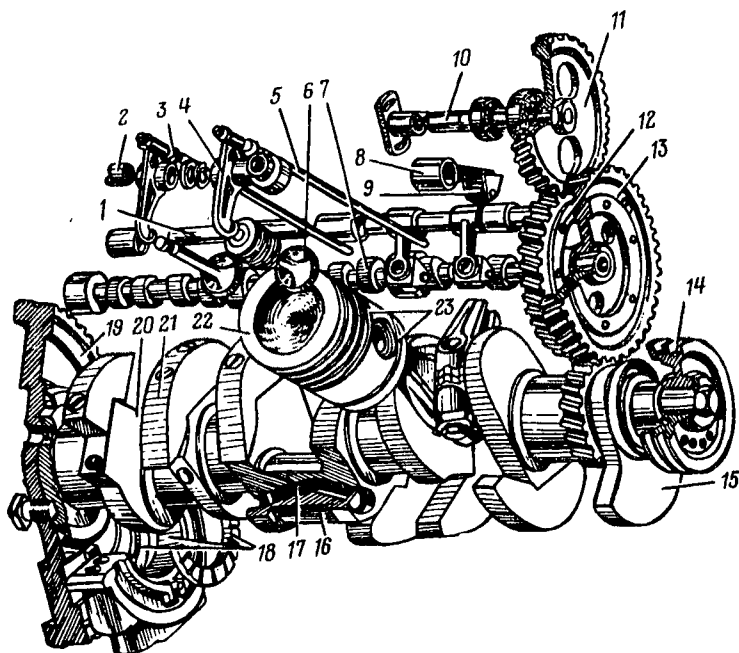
Кривошипно-шатунный и газораспределительный механизмы двигателя.
